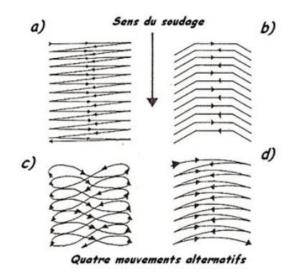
Les mouvements alternatifs de soudage [22]
